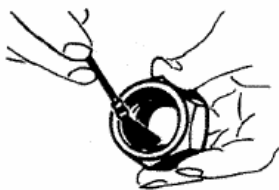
Резьбу накидной гайки хорошо смазать маслом, а не консистентной смазкой
